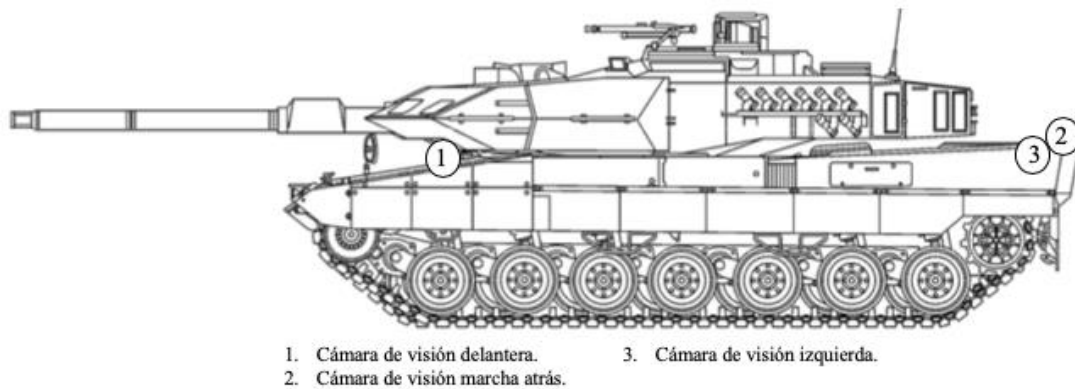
Vista de perfil de la instalación de las cámaras en el CC Leopard 2E. Fuente: Elaboración propia.
